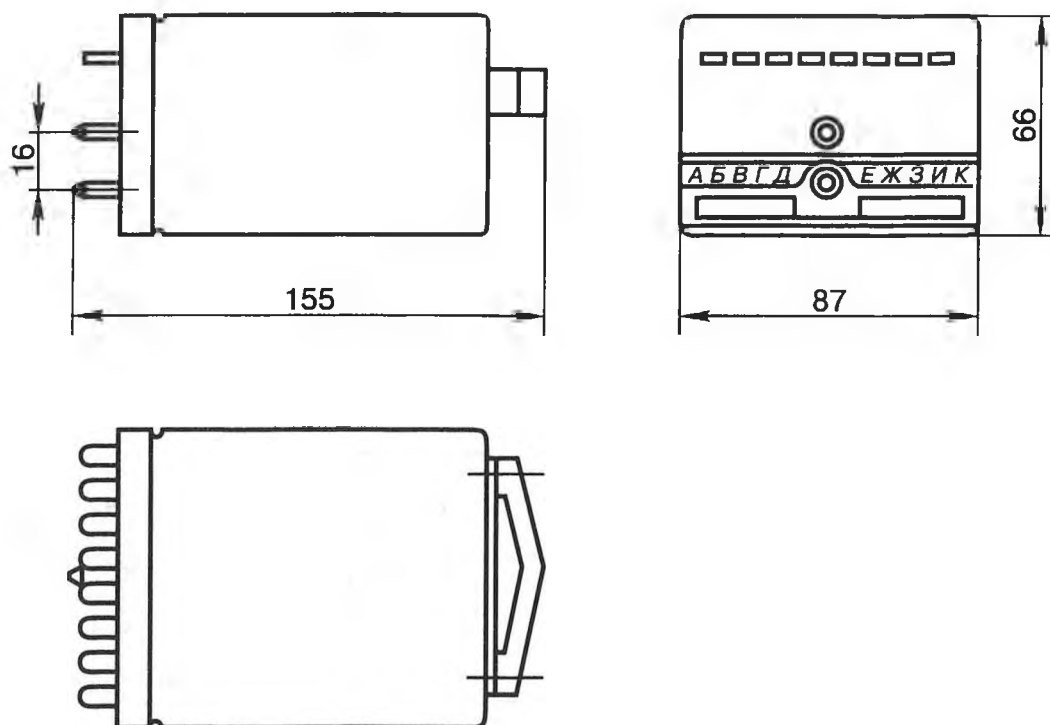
Габаритный чертеж реле типов РНМ1, РНМ3, РНМ3-У
